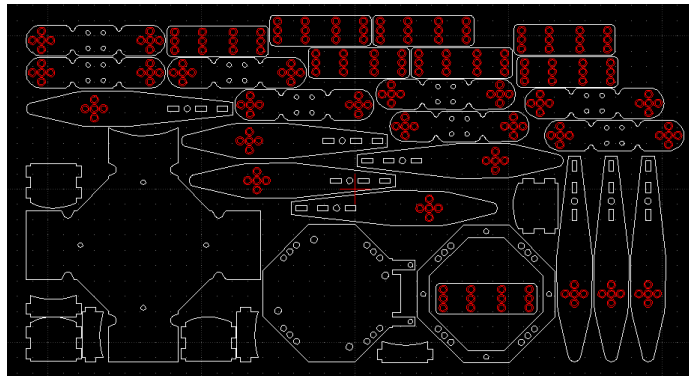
Motif à découper au laser pour produire les pièces du robot.
